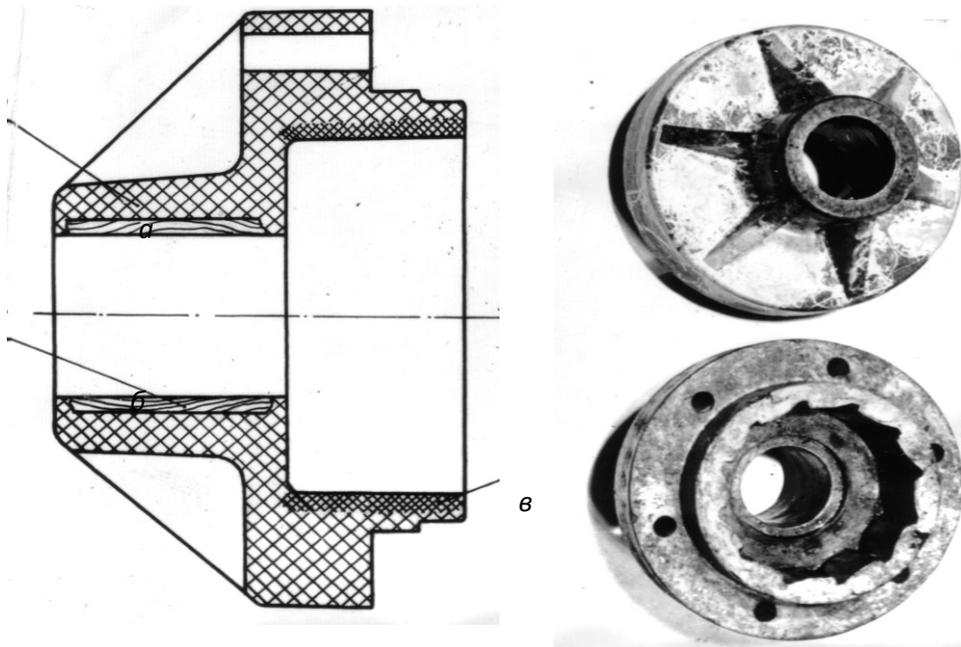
Корпус муфты свободного хода привода комбайна: а – корпус муфты; б – подшипник скольжения; в – зубчатый венец
